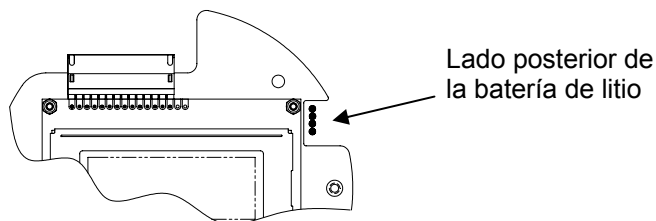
(Terminaciones de soldadura de la batería de litio)
